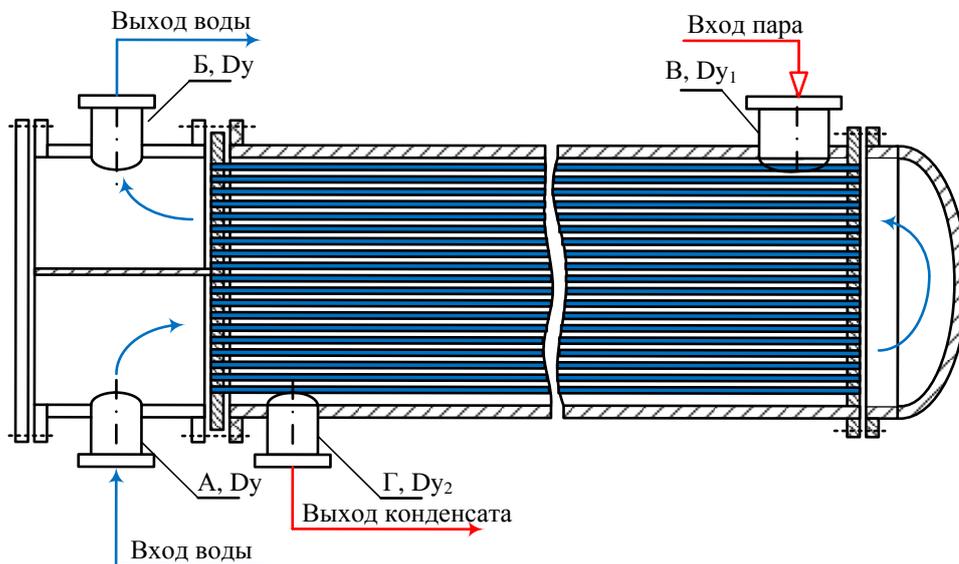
Горизонтальный двухходовой кожухотрубчатый конденсатор
